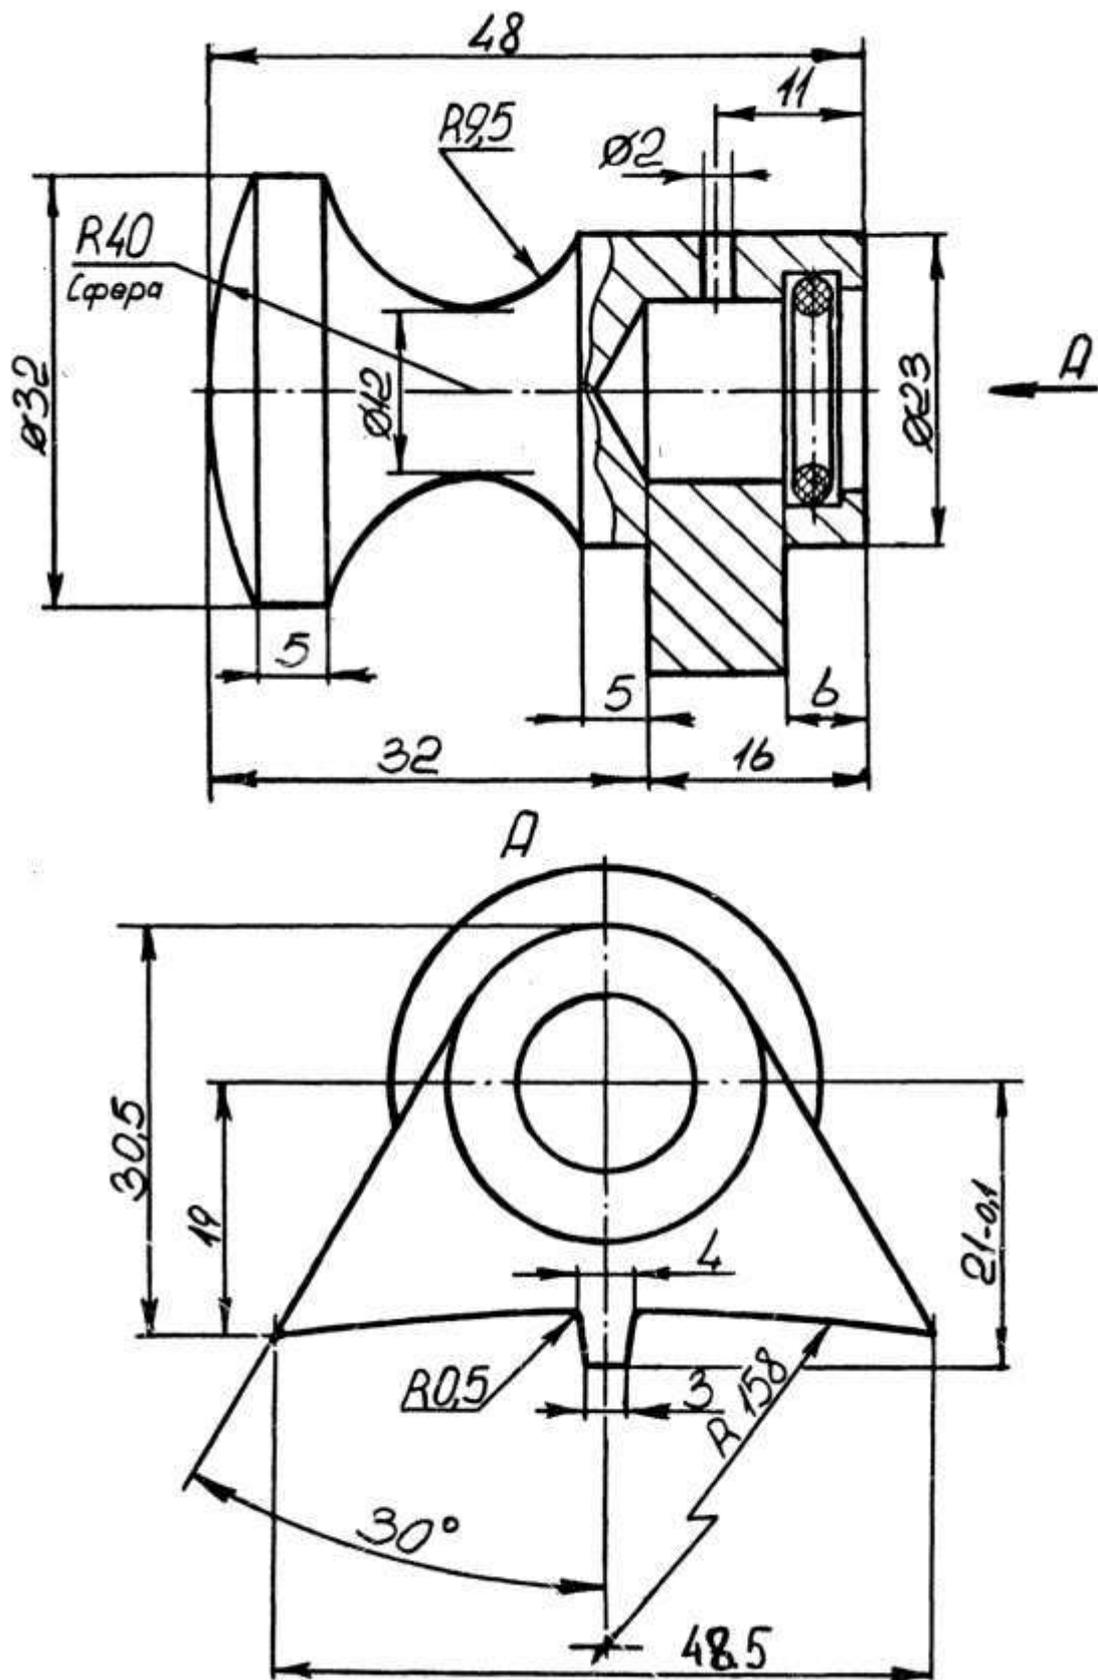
3М 7820-4550 Фиксатор коленчатого вала
